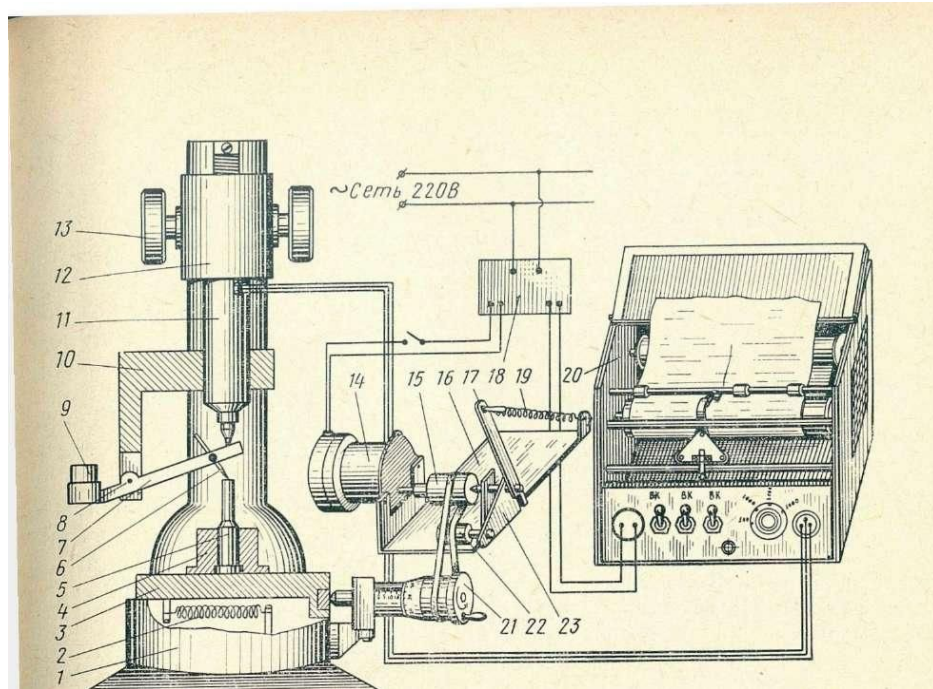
Принципова кінематична схема прибору для виміру зносу робочих частин розділового штампу
